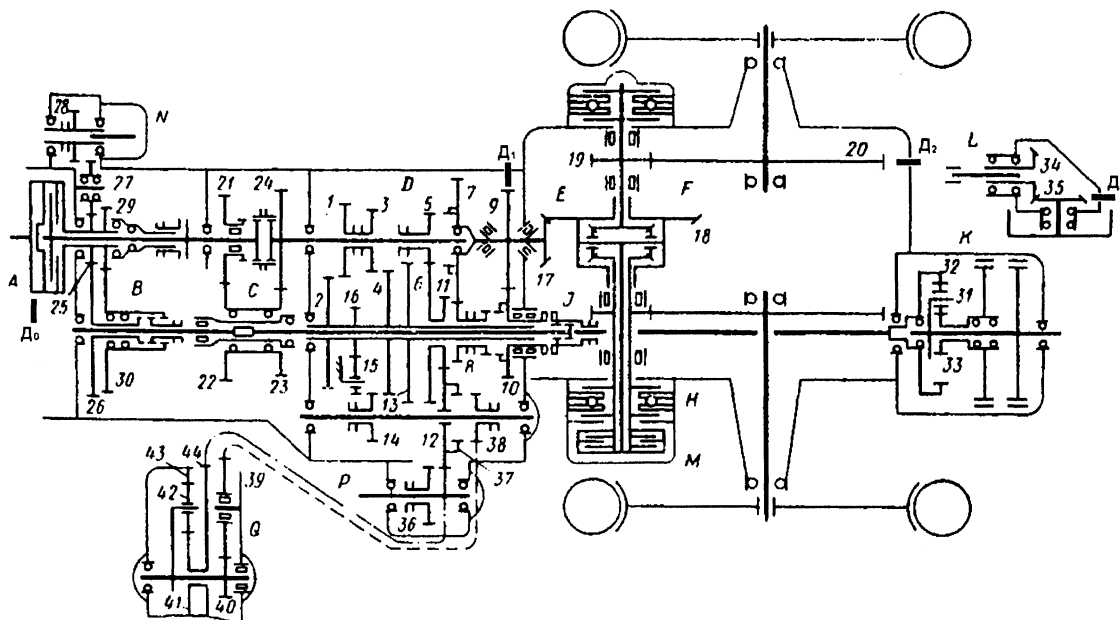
Кинематическая схема трансмиссии трактора МТЗ-80 и расположение датчиков
